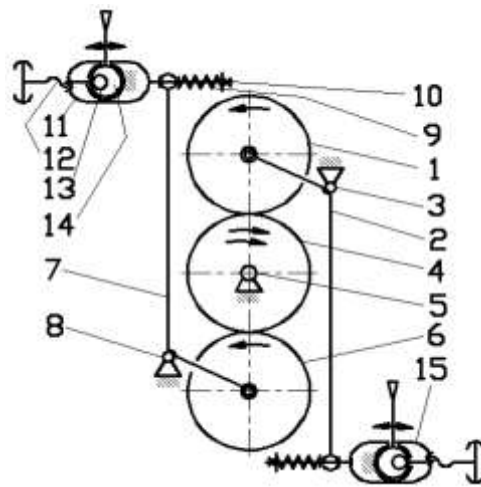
Схема установчого механізму багатостадійного верстата.
